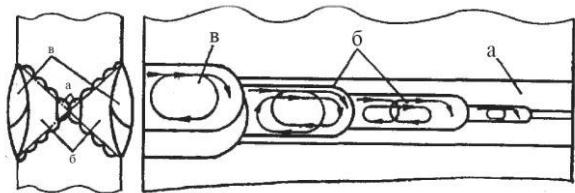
Перемещение горелки при механизированной сварке многослойныхстыковых швов в углекислом газе: а – первый слой; б – заполняющий слой; в – замыкающий слой
